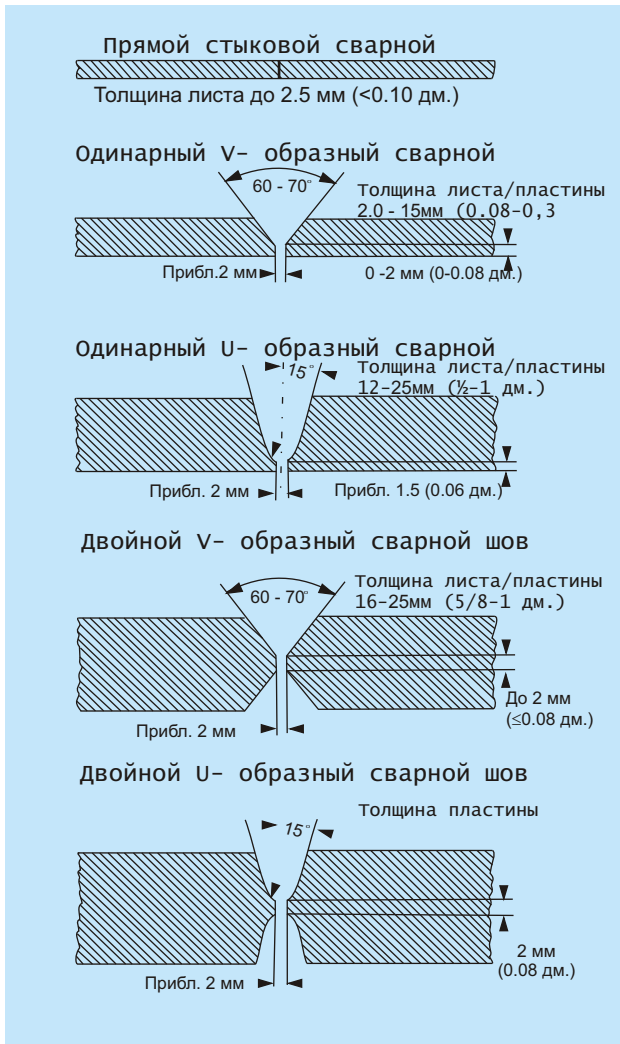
Подготовки кромок для сварки никелевых сплавов и специальных высококачественных сталей.
